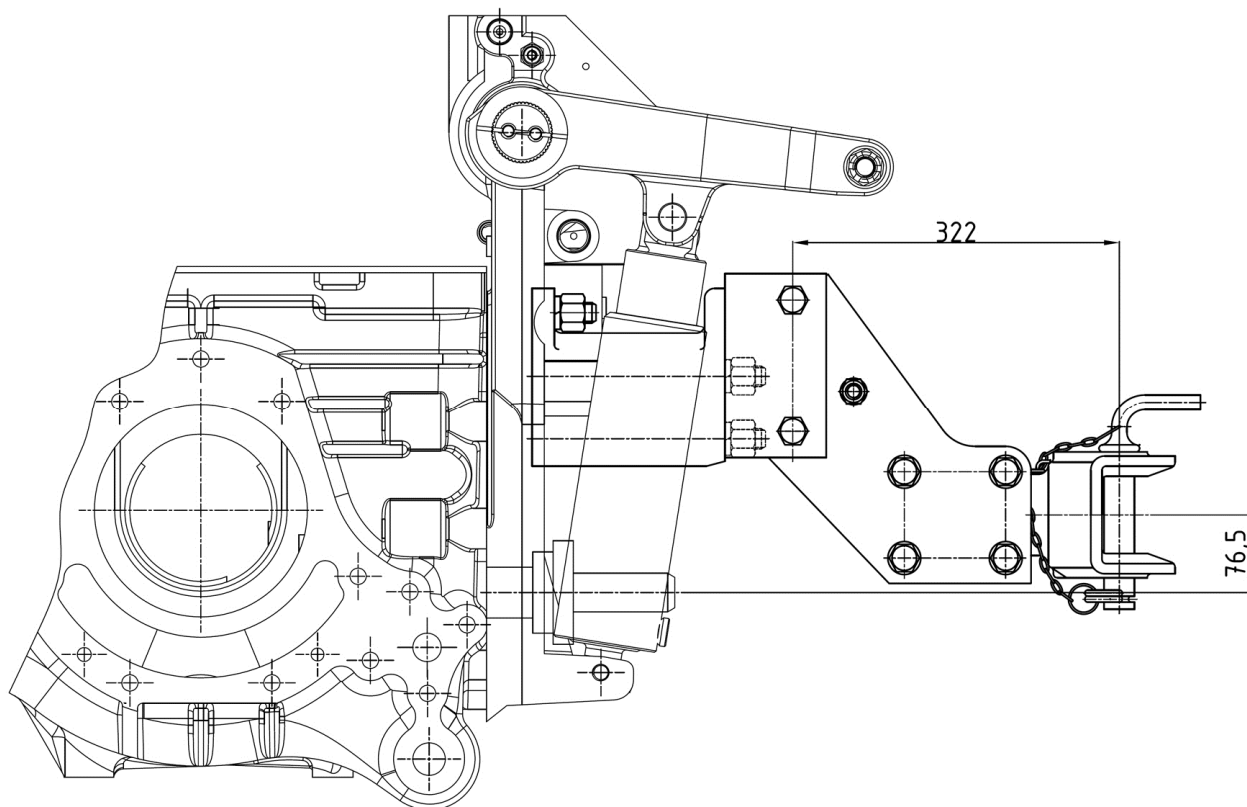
Схема установки ТСУ-3В (тяговой вилки длинной)
